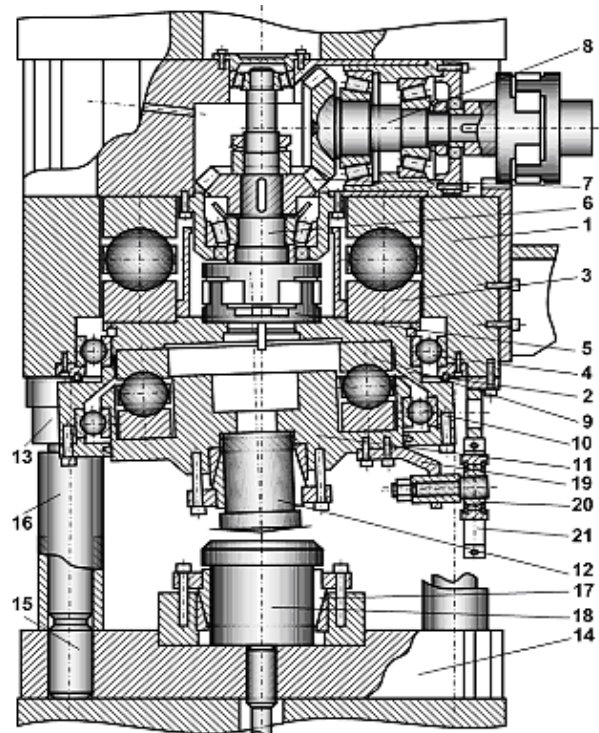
Конструкция блока для ШСО мод. БШО-50/280
